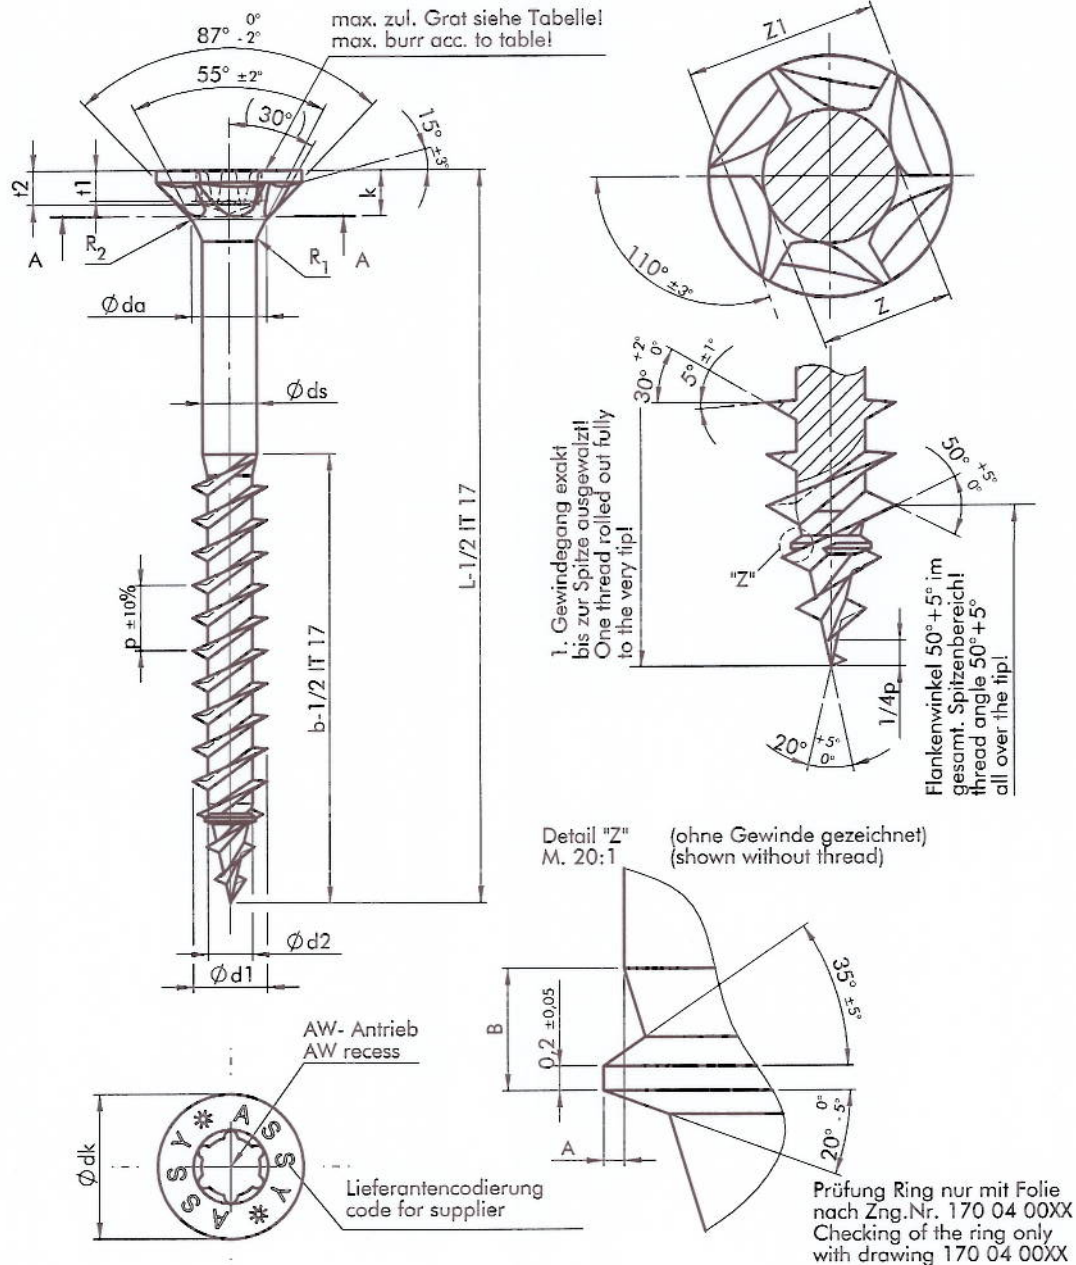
Geometrie der modifizierten ASSY 3.0 Schraube Durchmesser 3,0 bis 4,5 mm
